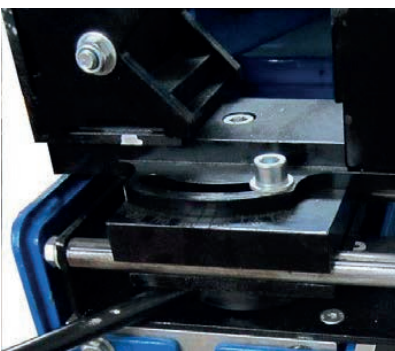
Dispositif d'inclinaison de la pièce à usiner
